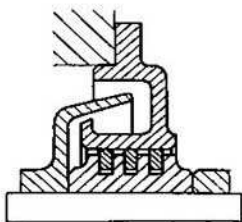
Empaquetadura combinada: disco deflector, empaquetadura con anillos seccionados de resorte
